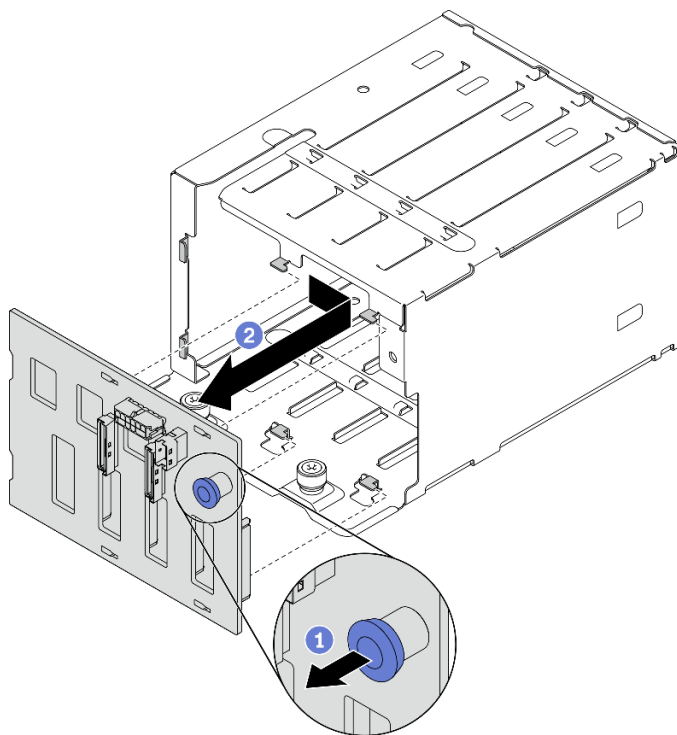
Entfernen der Rückwandplatte für 3,5-Zoll-Laufwerke
